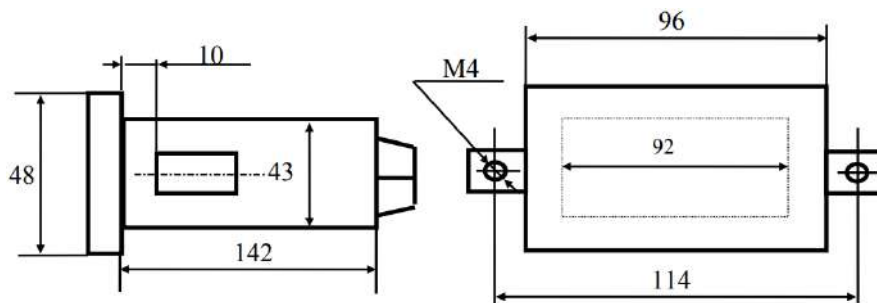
Габаритные размеры, корпус 48x96x155 мм
